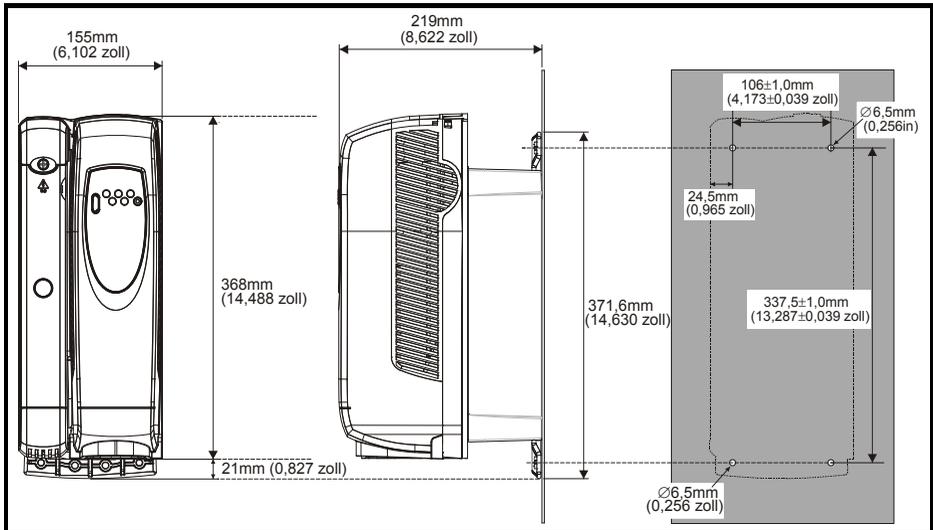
Rückwandmontage für Umrichter der Baugröße 3
